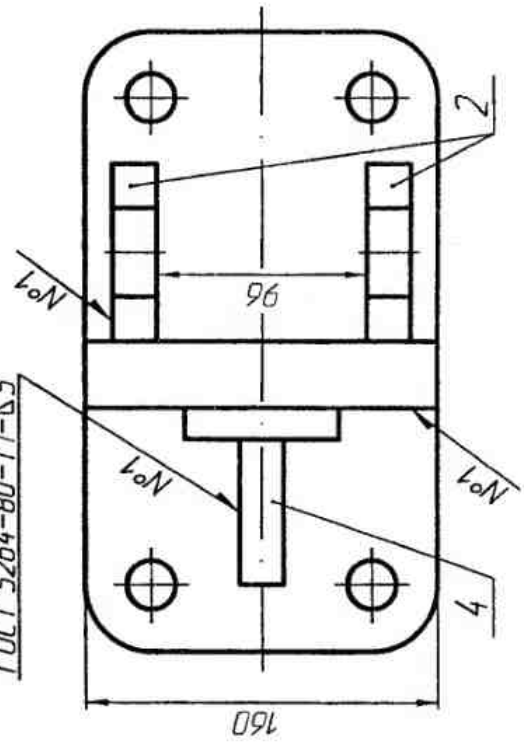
Изображение деталей для выполнения сварного соединения
